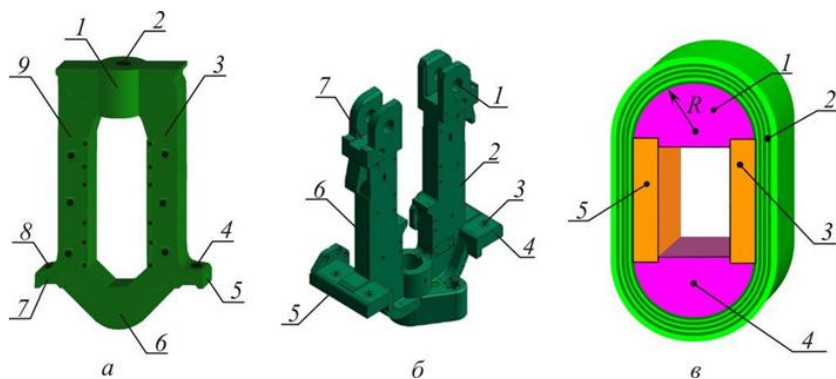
Типы станин: *а* – закрытая (1 – верхняя поперечина; 2 – отверстие под нажимной винт; 3, 9 – стойки; 4, 8 – отверстия под фундаментные болты; 5, 7 – лапы; 6 – нижняя поперечина); *б* – открытая (1 – отверстие для крепления верхней поперечины; 2, 6 – стойки; 3 – отверстие под фундаментный болт; 4, 5 – лапы; 7 – паз для установки верхней поперечины); *в* – составная (1, 4 – ригели; 2 – пакет металлической ленты; 3, 5 – стойки)
